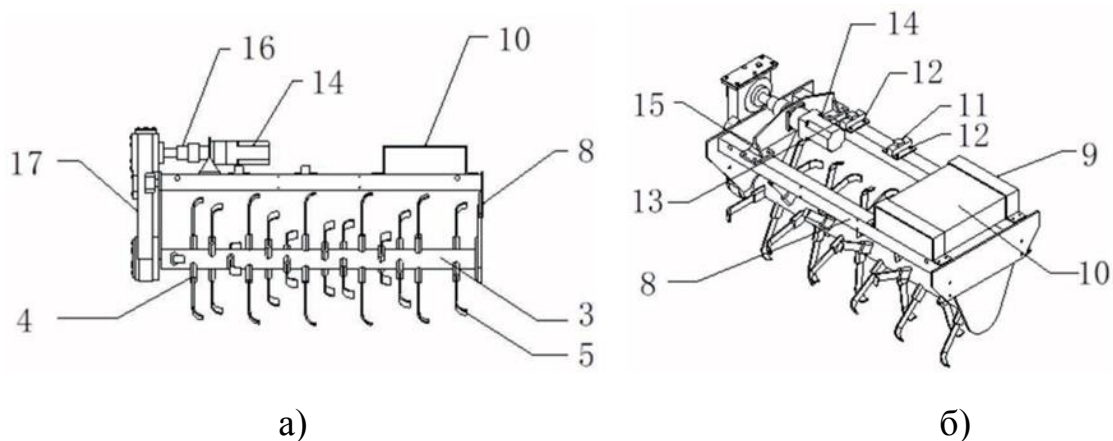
Общий вид роторного культиватора с приводом от электродвигателя:
